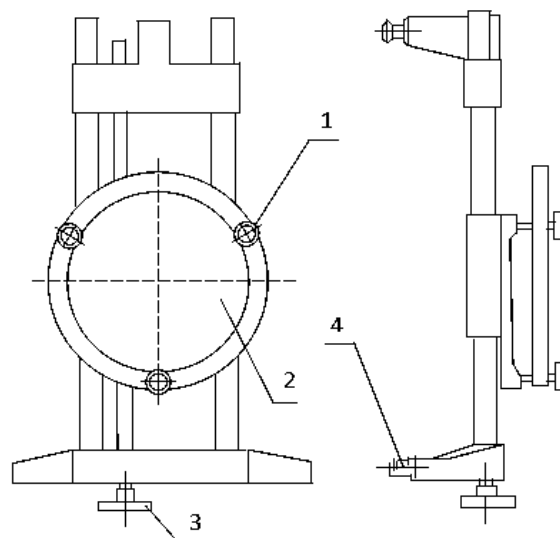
Розпірна консоль колісного блоку: 1 – дзеркала; 2 – регулювальна гайка; 3 – ручка ходового гвинта; 4 – упорний гвинт
